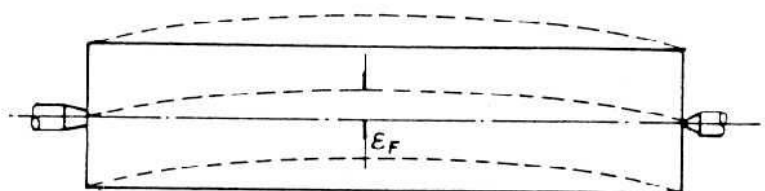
Desvio de fixação na usinagem de eixos esbeltos, por flambagem. (FERRARESI, 1970)
